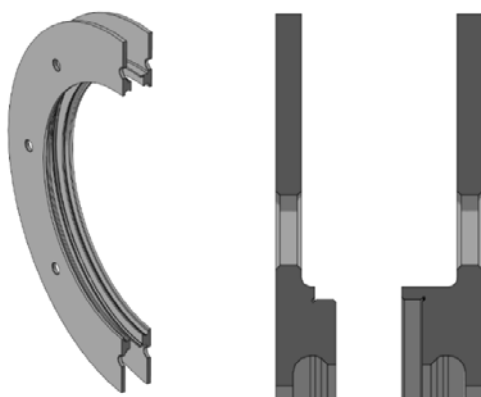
Кольцевые образцы-имитаторы для отработки режимов сварки
